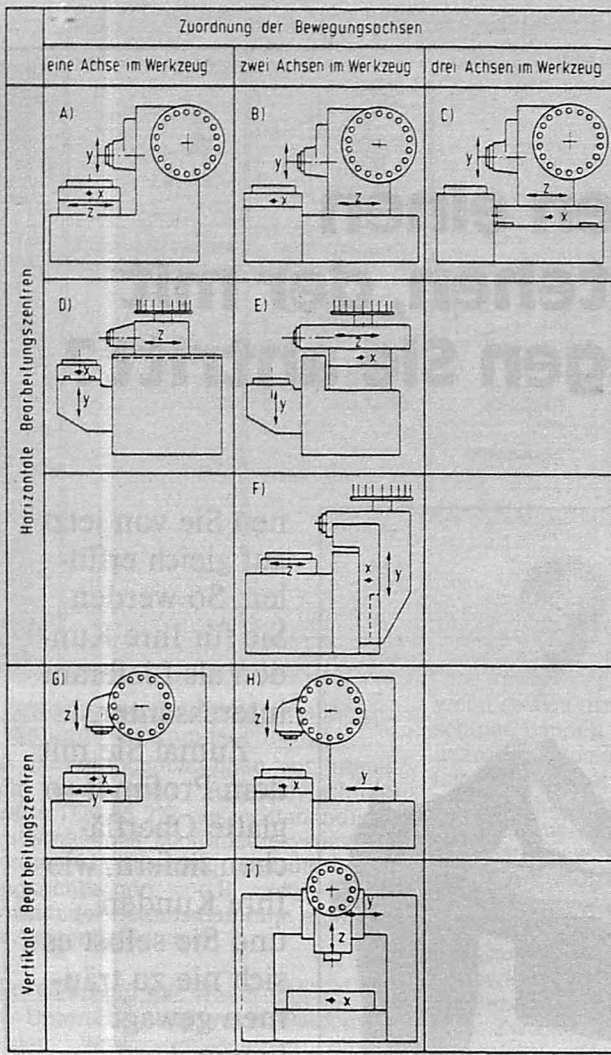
Bauformen von Bearbeitungszentren für die Metallbearbeitung [6] Einstanderbauweise mit horizontaler Hauptspindel; A) bis C): Einstanderbauweise mit horizontaler Hauptspindel; D) bis F): Konsolbauweise; G) bis H): Einstanderbauweise mit vertikaler Hauptspindel; I): Portalbauweise.
